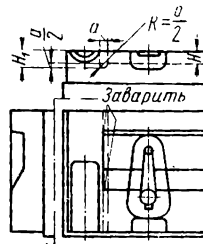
Замок, изготовленный строжкой до канавки для выхода резца
